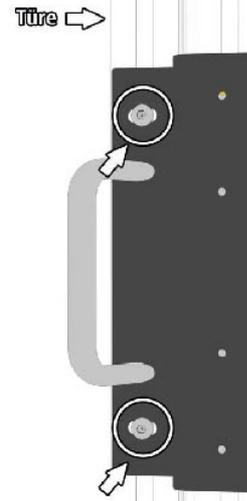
Montageplatte mit Ankerplatte am Profil anbringen und zur Prozesszuhaltung ausrichten. Schrauben M8 x 12 mm Torx festziehen.
